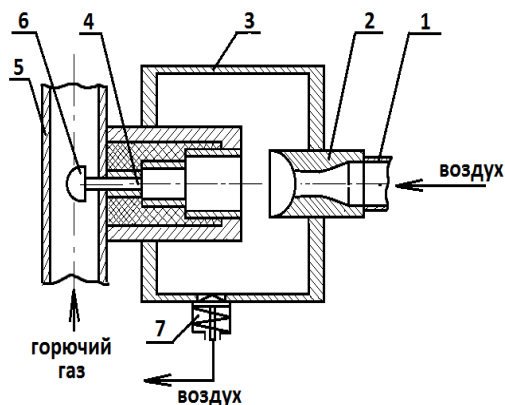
Газодинамический воспламенитель: 1 – воздухопадающая труба; 2 – сопловой насадок; 3 – акустическая камера; 4 – резонансная трубка; 5 – топливоподающая труба; 6 – излучатель; 7 – обратный клапан
